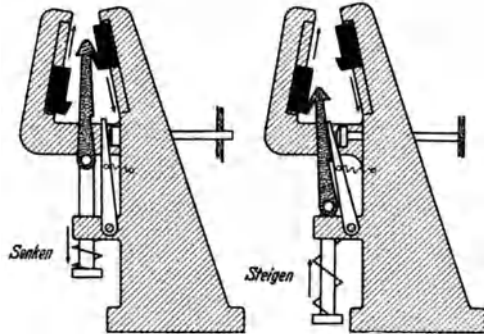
Rechte Schaufel mit Platine oben, Loch in der Karte. Schaft wird sinken.
